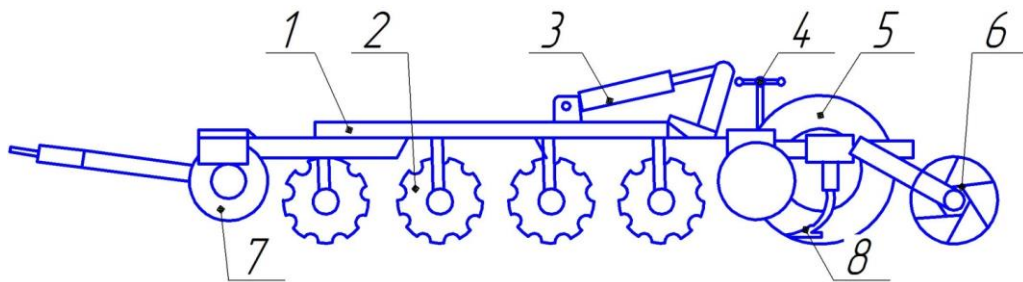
Схема борони [патент № 78394]: 1 – рама; 2 – диск; 3 – гідроциліндр; 4 – ручка; 5 – транспортне колесо; 6 – коток; 7 – копір; 8 – розрихлювач
